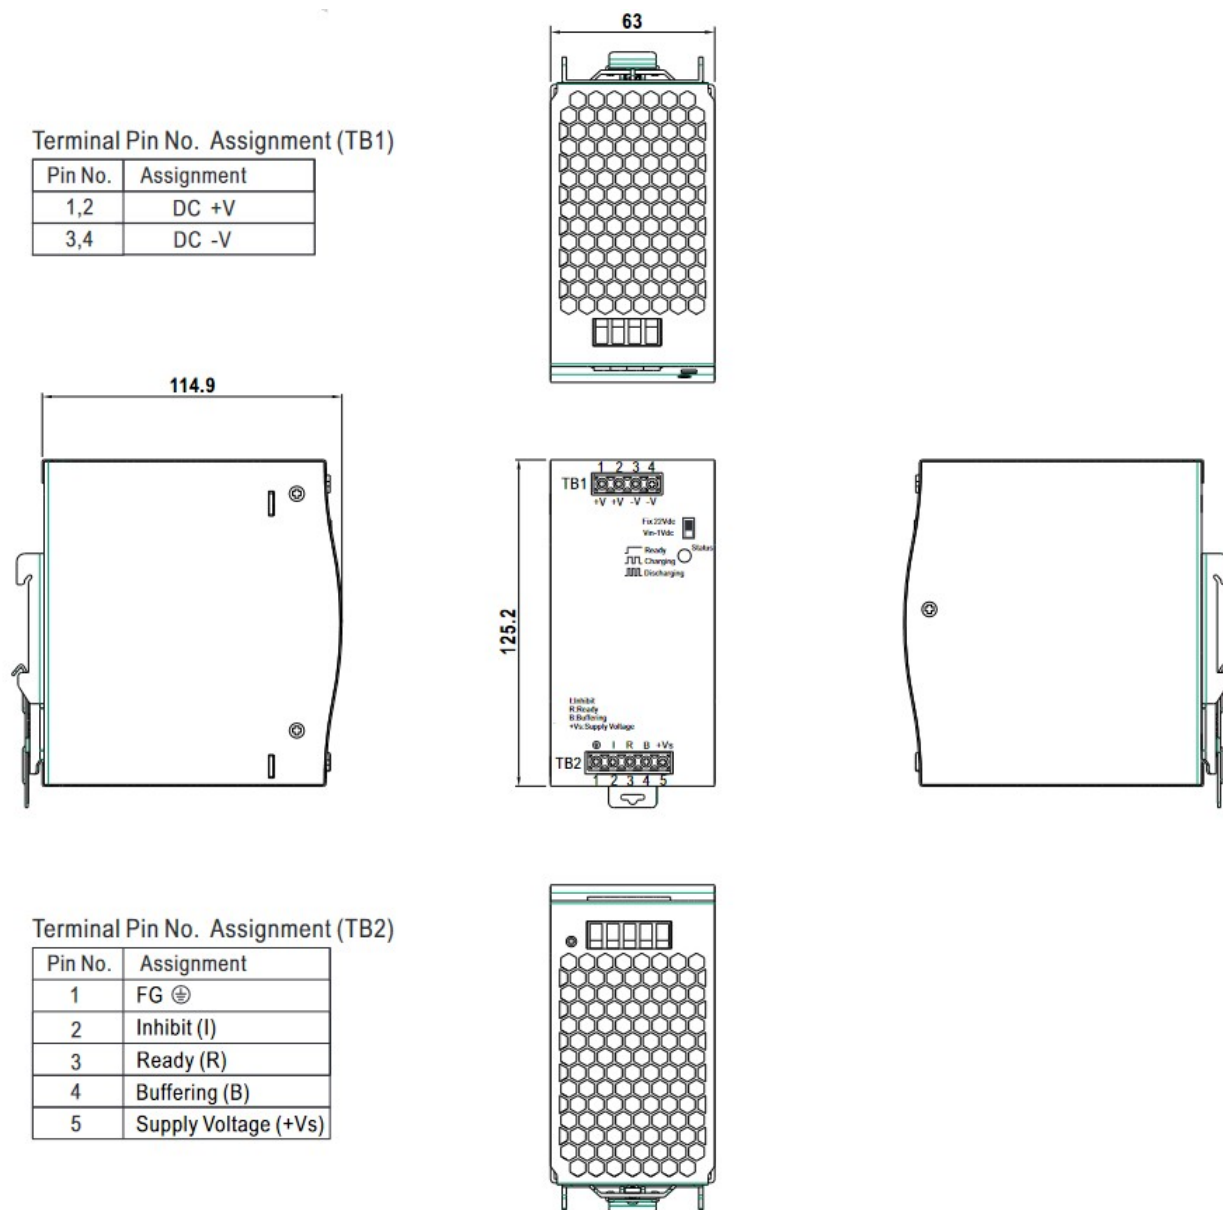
Габаритные и установочные размеры буферного блока питания DBUF20-24 и DBUF40-24
